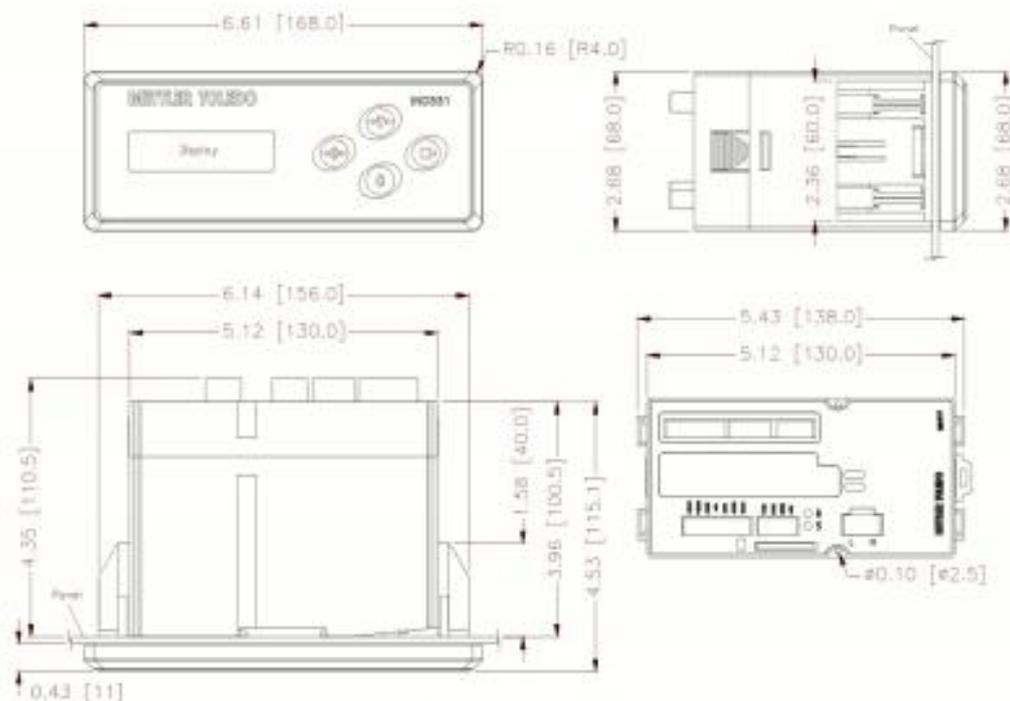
Dimensiones del gabinete de montaje en panel de la IND331
